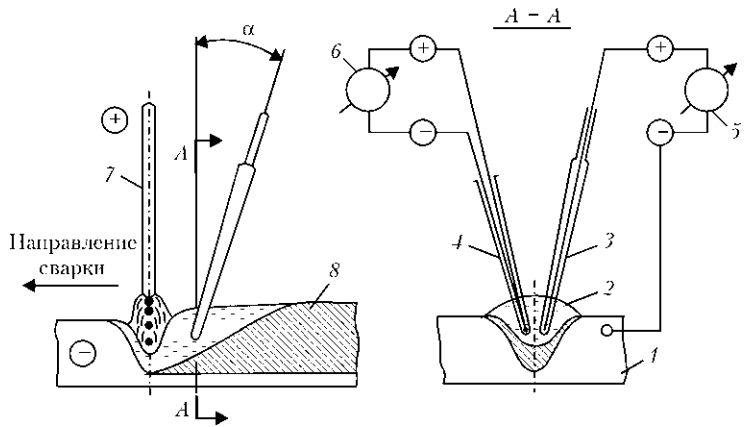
Принципиальная схема экспрессного контроля активности кислорода в металле сварочной ванны: 1 — свариваемый металл; 2 — сварочная ванна; 3 — датчик окисленности; 4 — термопара; 5, 6 — измерительные приборы; 7 — сварочный электрод; 8 — сварной шов; α — угол наклона датчика и термопары, равный 15...20°
